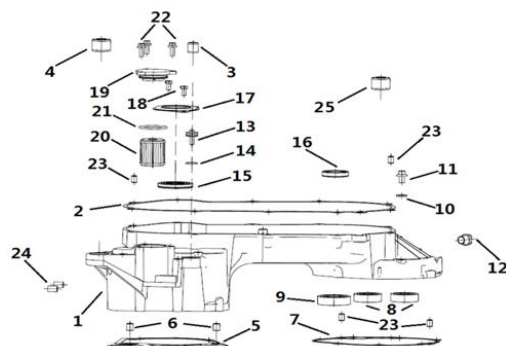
CARCASA MOTOR IZQUIERDA
